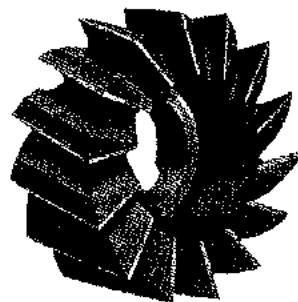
Fresa cilíndrico-frontal (Union Twist Drill Co.)
